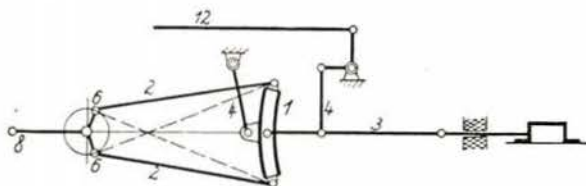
Schemaskizze zu der Gooch-Steuerung (aus: Henschel-Lokomotiv-Taschenbuch)
